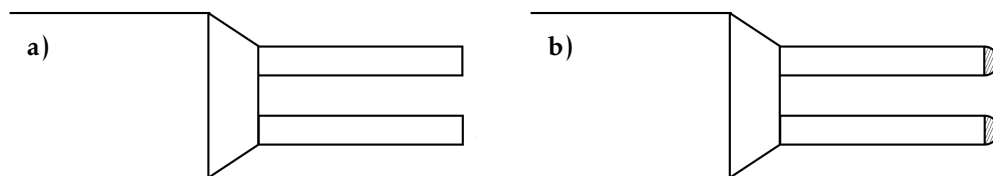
a) Condición inicial de la probeta después de realizar la adecuada limpieza y b) Probeta con hemisferio de soldadura en cada aguja.
